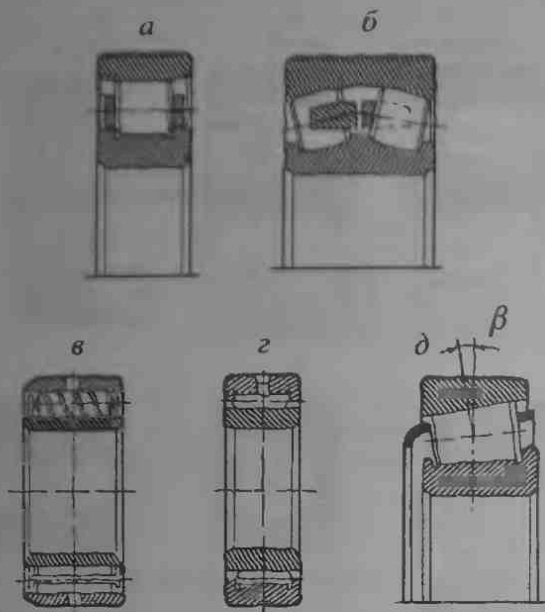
Типичные конструкции роликовых подшипников качения: а) радиальный с короткими цилиндрическими роликами; б) радиальный цилиндрический двухрядный; в) с витыми роликами; з) игольчатый; д) конический однорядный
